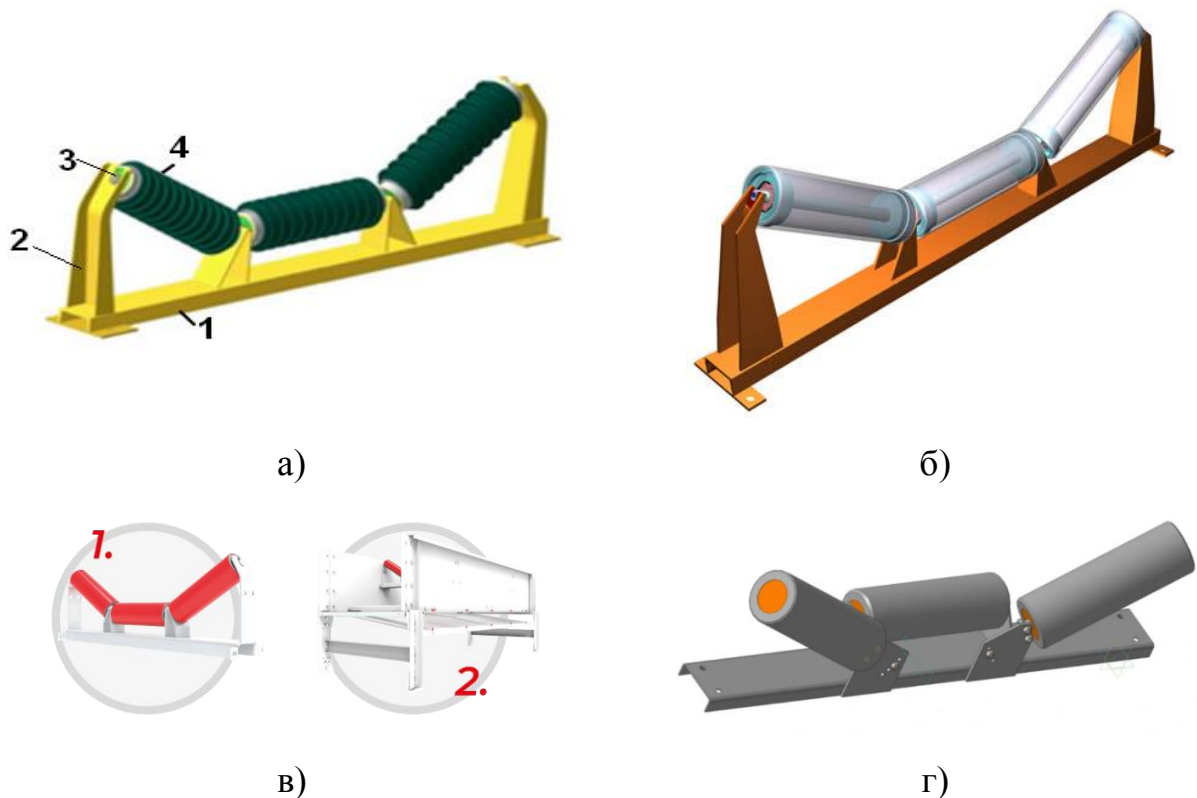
Загальний вигляд конструкцій роликів опор:
